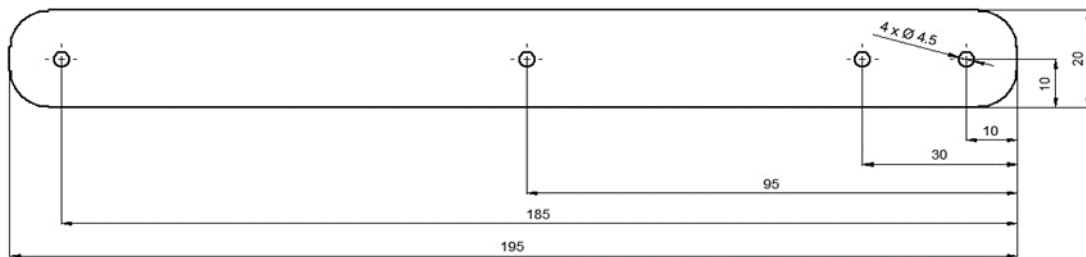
Konstrukcja metalowa ortezy na rękę i przedramię w rozłożeniu – widok zewnętrznej strony ortezy
